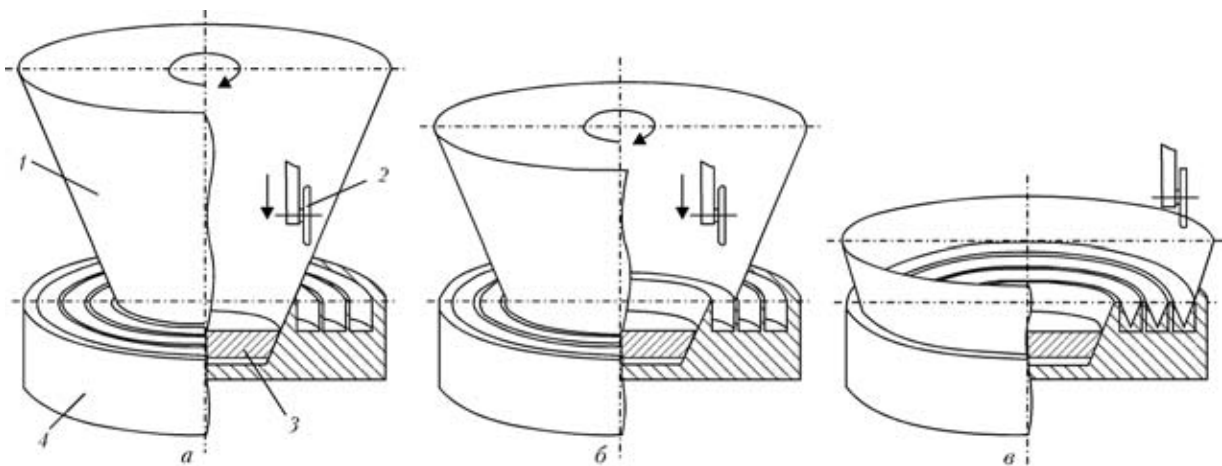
Схема преобразования конической оболочки в гофрированный диск соответственно на начальном (а), промежуточном (б) и завершающем (в) этапах: 1 — коническая заготовка; 2 — формирующий ролик; 3 — прижим для закрепления заготовки на форме; 4 — форма-матрица
